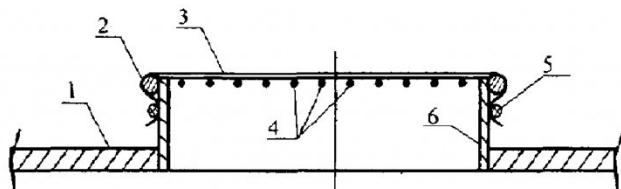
Схема вышибной заглушки: 1 - корпус СВГС; 2 - ват-тканцовка; 3 - прорезиненная ткань - мембрана; 4 - решётка; 5 - стяжёлая мкта; 6 - патрубок
